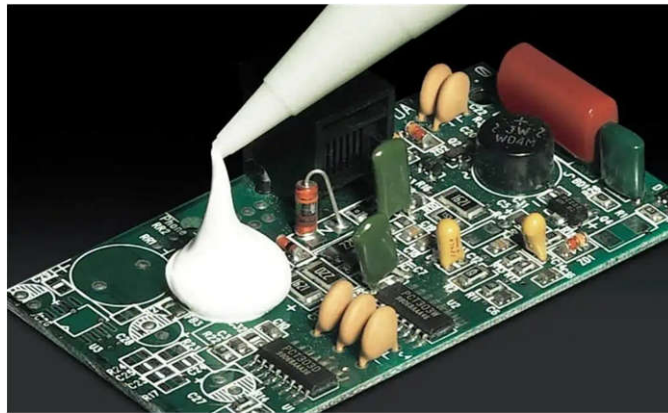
用于降低污染等级的 PCB 敷形涂层
